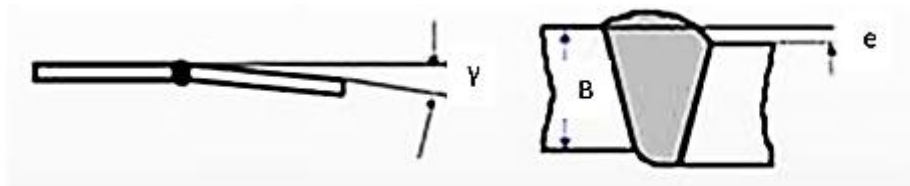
Définitions des défauts d'alignement dans les joints soudés
